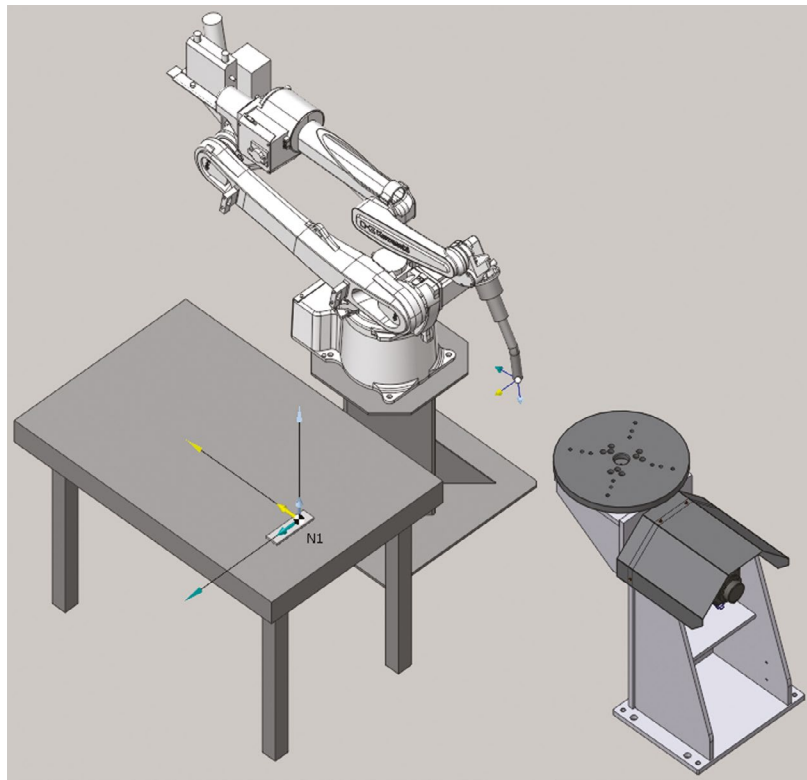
Созданный цифровой двойник роботизированной ячейки в утилите MachineMaker.
